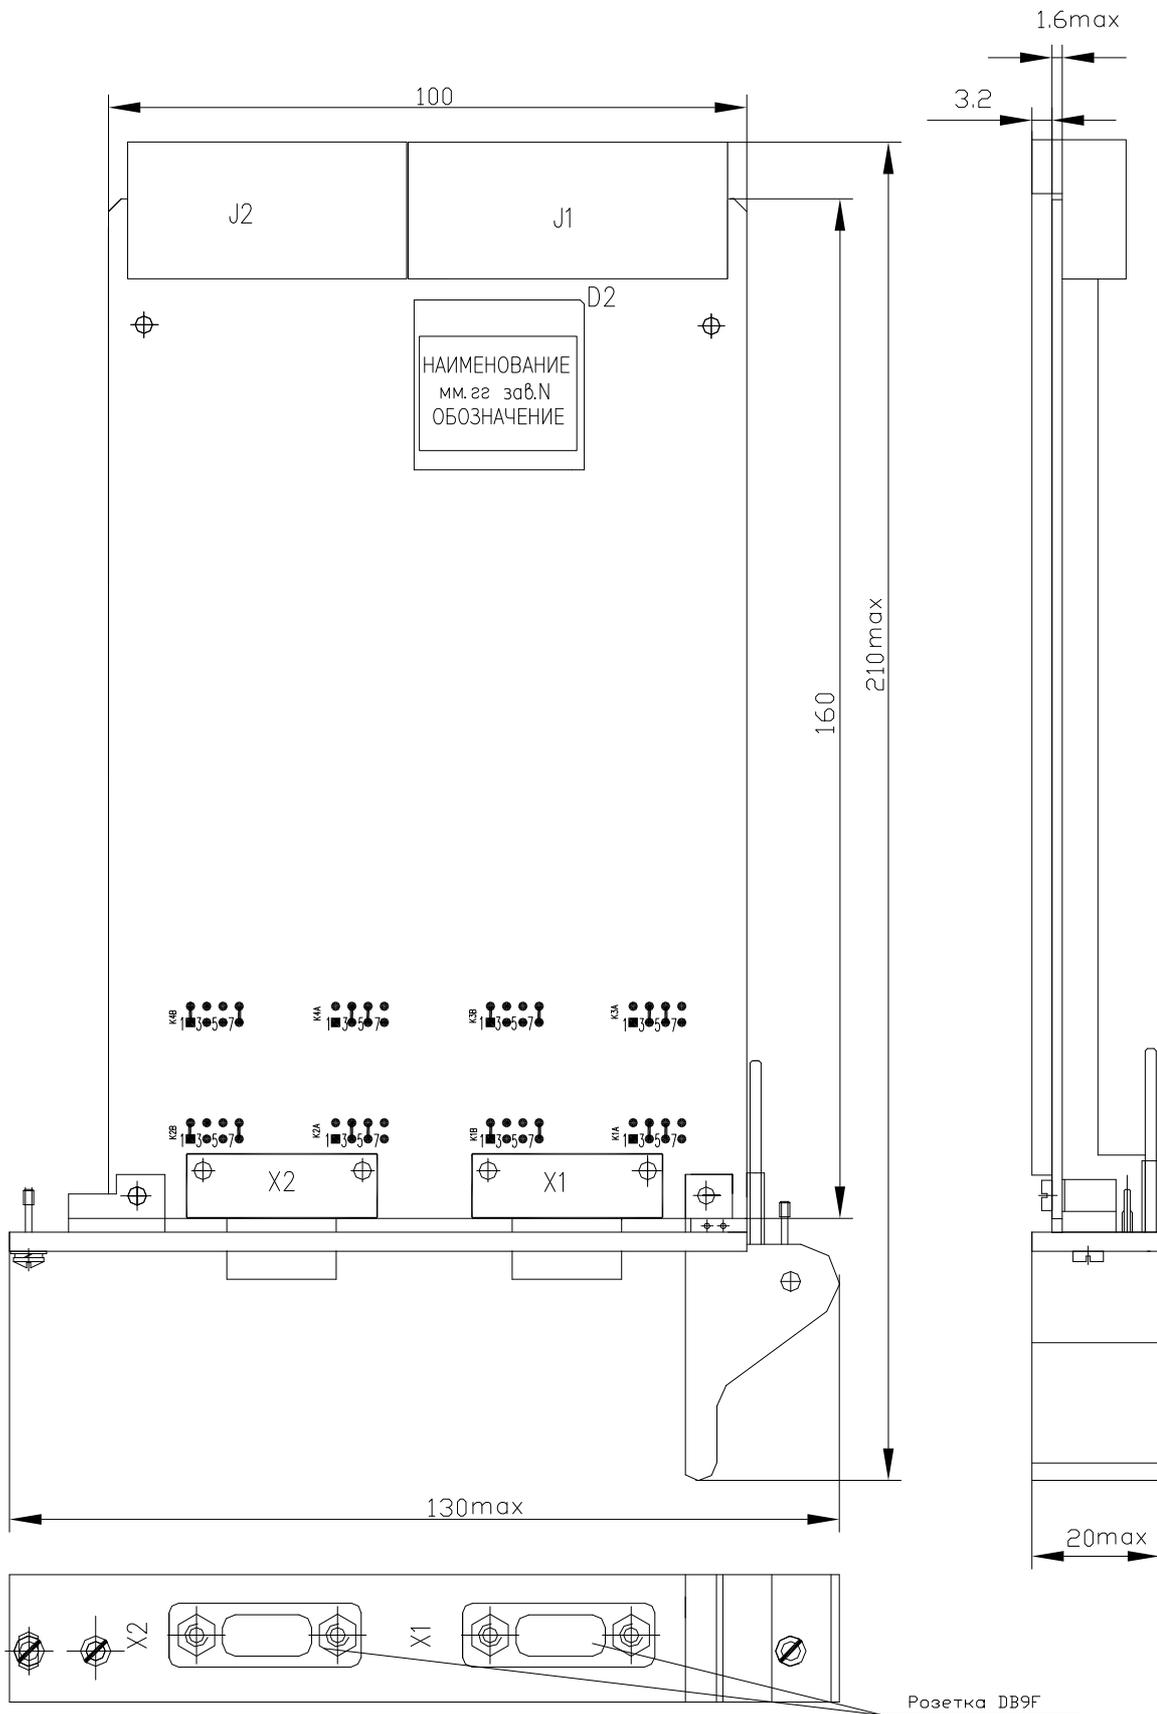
Габаритный чертеж для ТА1-3U-СРСІ-04-3 с запаянными перемычками
